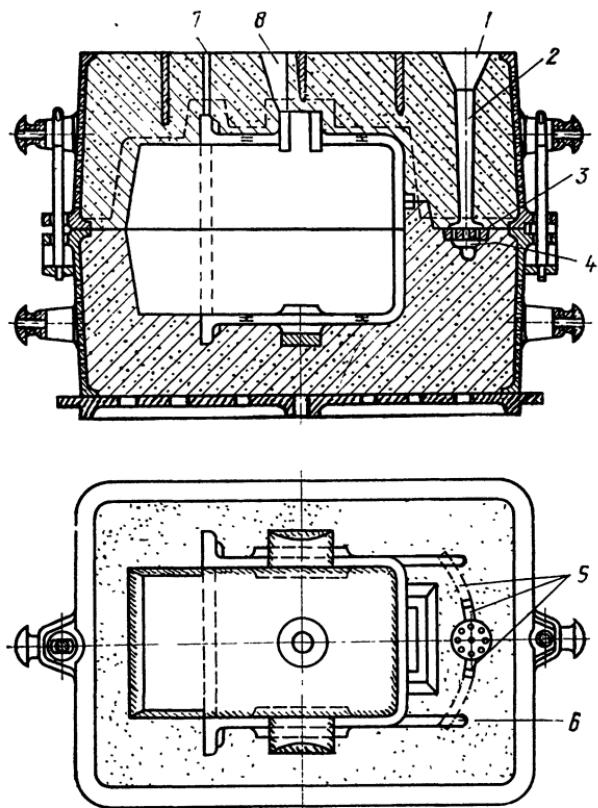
Песчаная форма с литниковой системой для отливки детали. Корпус из серого чугуна
